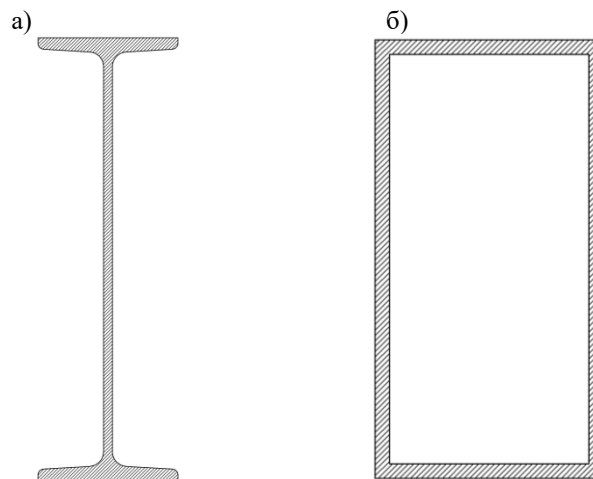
Переріз хребтової балки рами вагона-платформи
